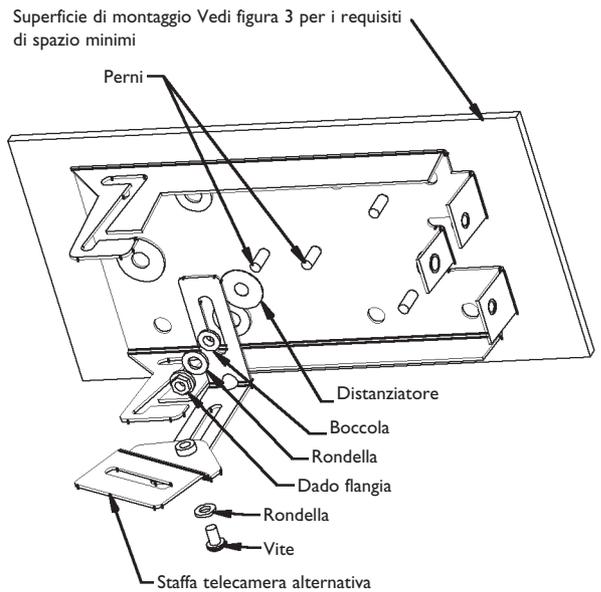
Montaggio del sistema di fissaggio con staffa alternativa
